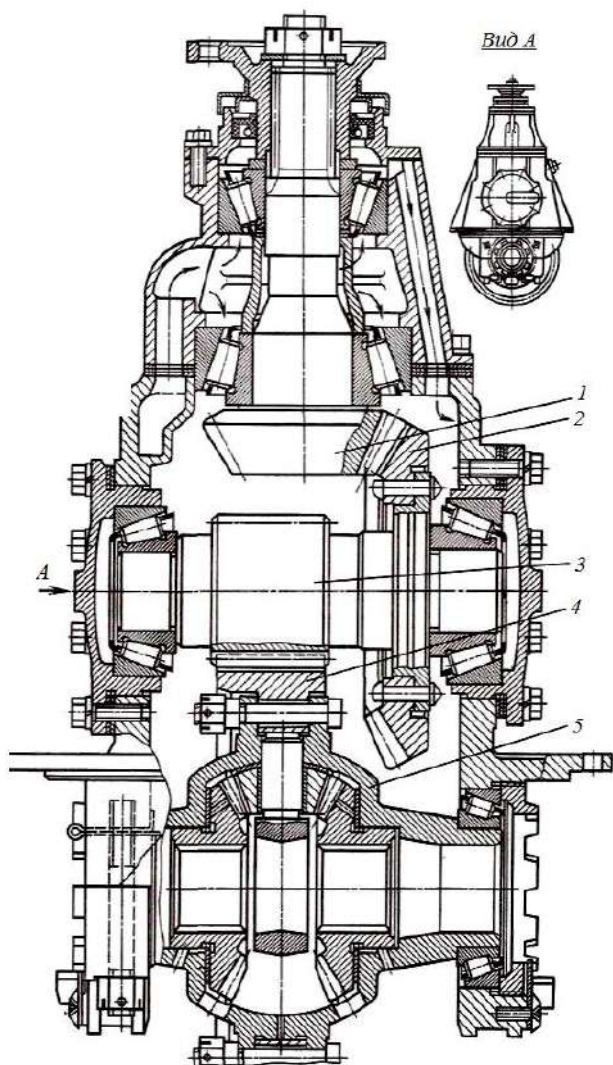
Центральна головна передача з валами, розташованими в одній площині: 1 – конічна шестерня; 2 – конічне колесо; 3 – циліндрична шестерня; 4 – циліндричне колесо; 5 – диференціал
